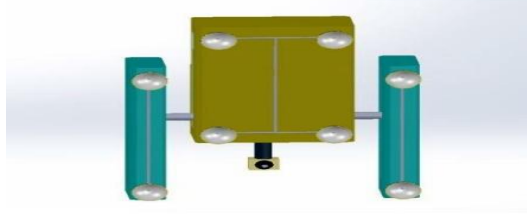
BioInMech Wall Climbing Robot [34]
